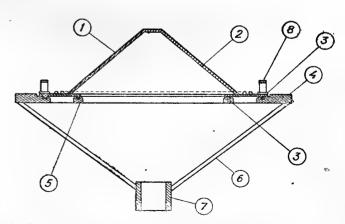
Головка аппарата для отливки дифузоров без шва: 1частая сетка с'емки части матрицы; 2-дыропробивная сетка с'емки части матрицы; 3—уплотняющее резиновое кольцо; 4—поддерживающее кольцо; 5—ребра поддерживающего кольца; 6—нижиий конус; 7-нтулка для присоединения головки к вакуумному насосу; 8—ручка
